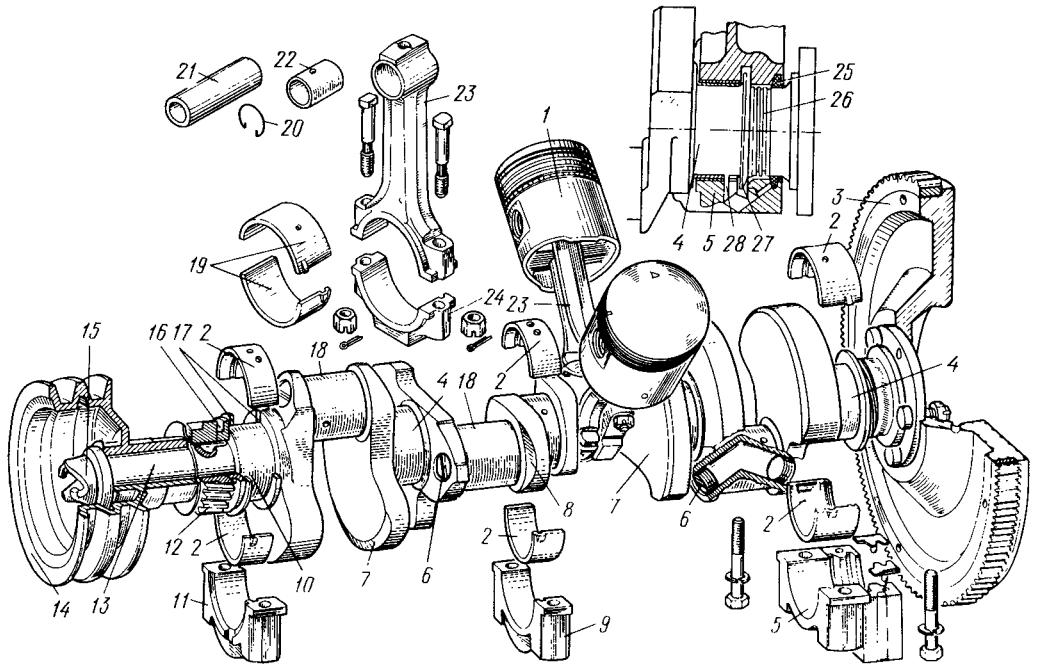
Детали кривошипно-шатунного механизма двигателя ЗИЛ-130:
